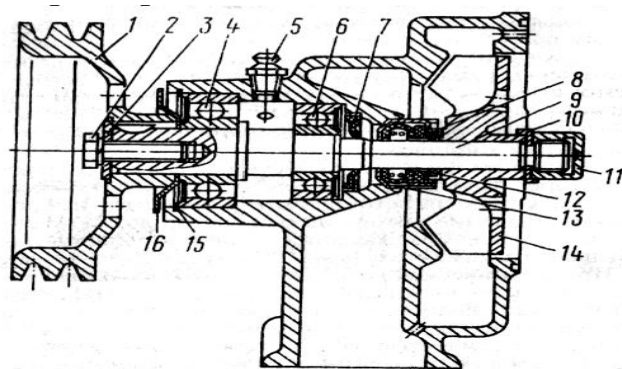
Насос водяной: 1 - шкив; 2 - болт; 3, 10 - шайбы; 4, 6 - подшипники; 5 - пресс-масленка; 7 - манжета; 8 - кольцо уплотнительное с обоймой; 9 - валик; 11 - гайка колпачковая; 12 - кольцо упорное; 13 - уплотнение (сальник); 14 - крыльчатка; 15 - кольцо стопорное; 16 - пылеотражатель;
